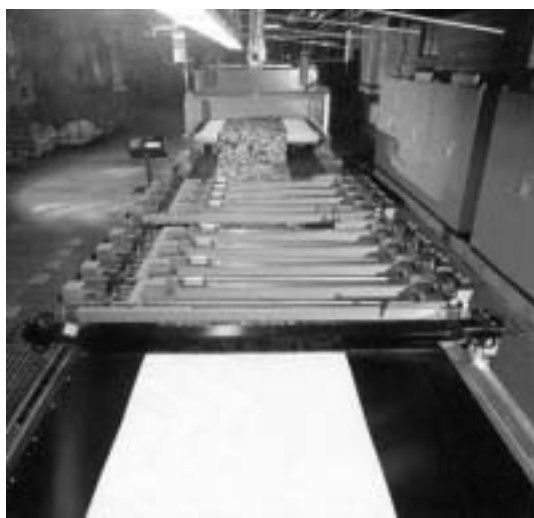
Immagini di macchine per stampa a cilindri cavi
